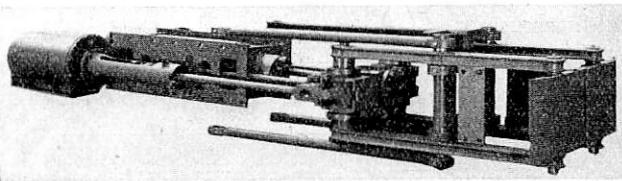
Seitlich ausschwenkbare Stoßplattengestänge mit Antrieb.
